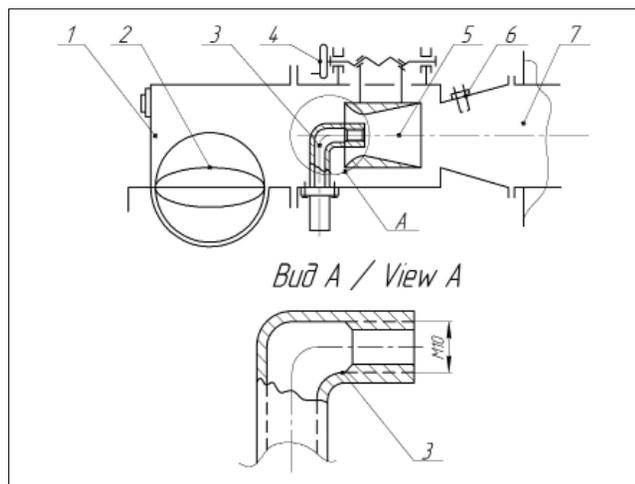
Схема горелки топочного агрегата ТБМ-1,7: 1 – вентилятор; 2 – заслонка; 3 – трубка форсунки; 4 – маховичок регулировки положения диффузора; 5 – диффузор; 6 – запальная свеча; 7 – топочный агрегат
